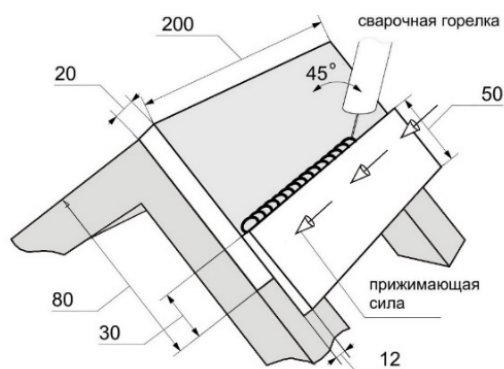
Схема сборки и сварки образца для определения склонности покрытия к порообразованию
